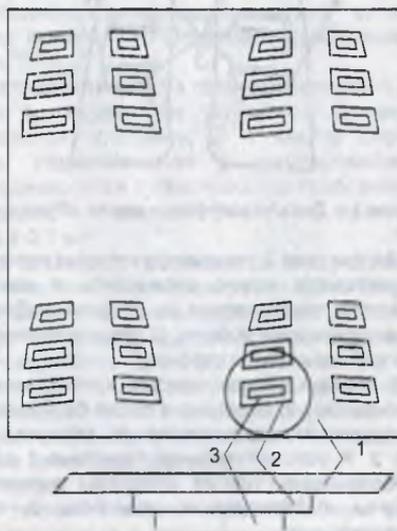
Вспомогательная пластина для базирования деталей (вид снизу)
